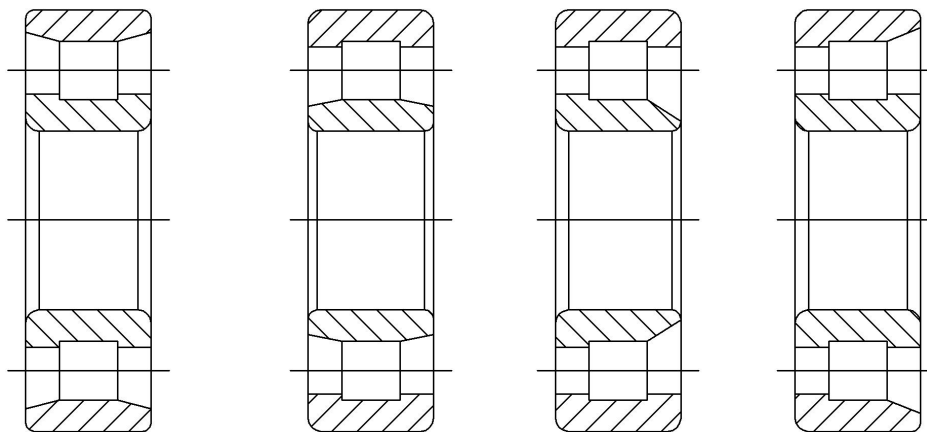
Роликові підшипники радіальні з короткими циліндричними роликами
